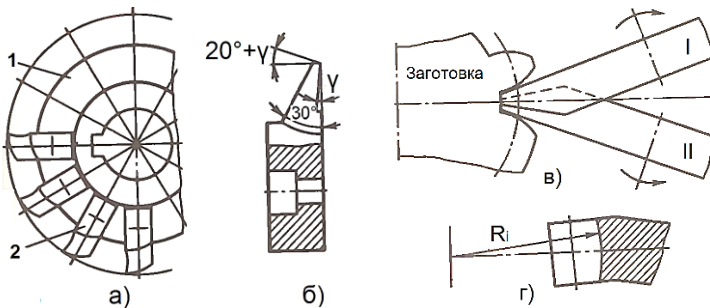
Схема фрезерування конічних зубчастих коліс методом обкату двома дисковими фрезами
